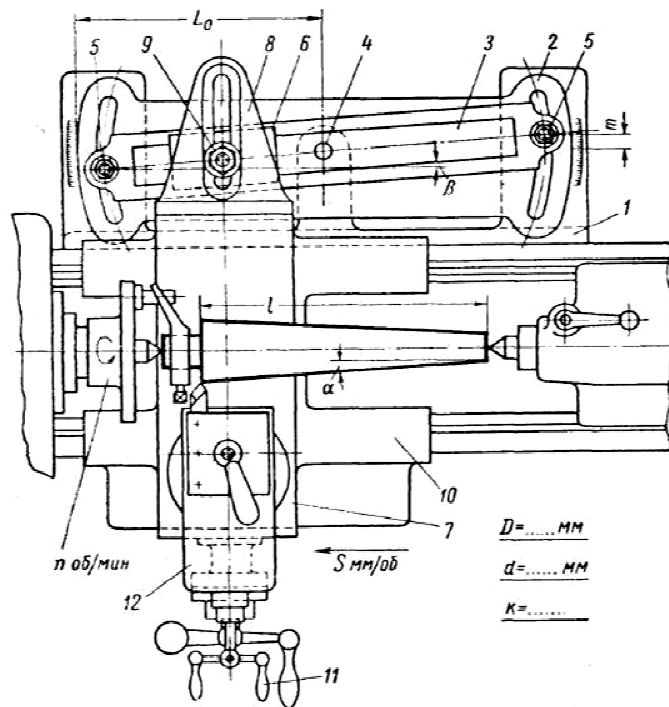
Схема наладки токарного станка на обработку конуса с помощью конусной линейки
